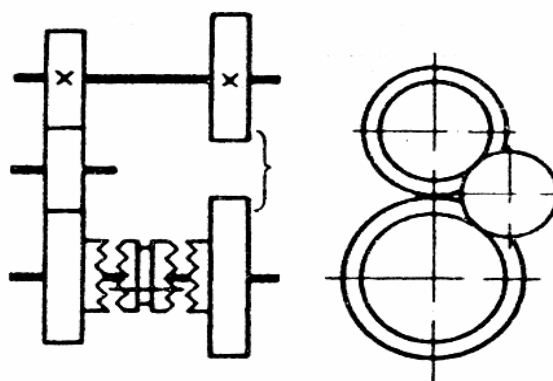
Реверсивный механизм с цилиндрическими колесами
